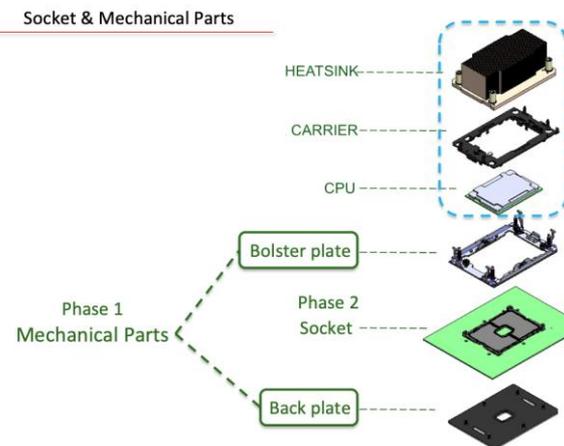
、CPU Socket 可再細分為 mechanical 與 Socket
